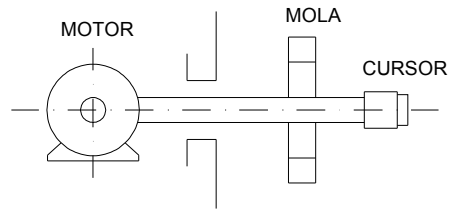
5 – Montagem da mola e motor do regulador de ação direta.
